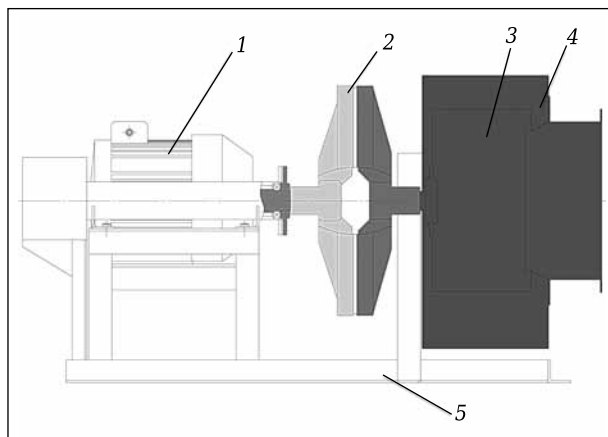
Схема устройства жарового вентилятора: 1 — двигатель; 2 — муфта; 3 — крыльчатка; 4 — улитка с воздухозаборником; 5 — рама
